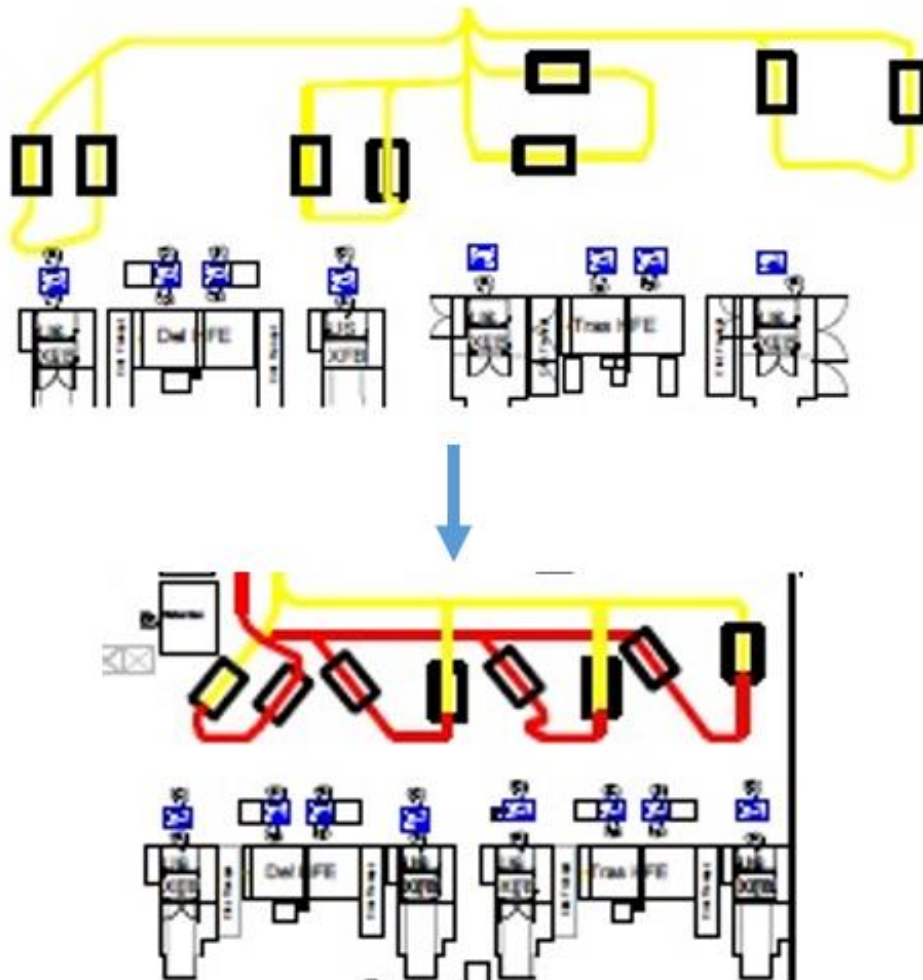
Modificación de la zona de ensamblaje y soldadura
